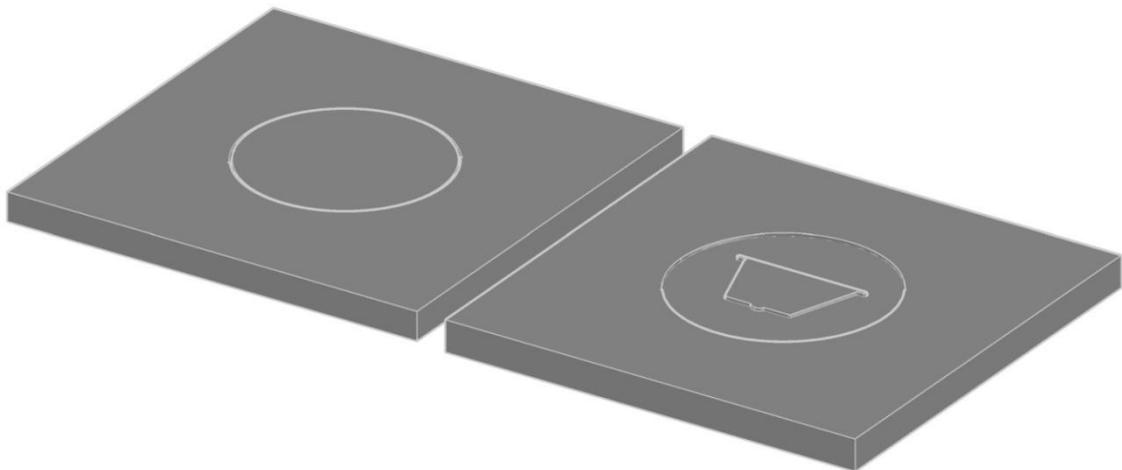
Molde para la pieza 1.1 tapa grande. Detalle del fresado.
